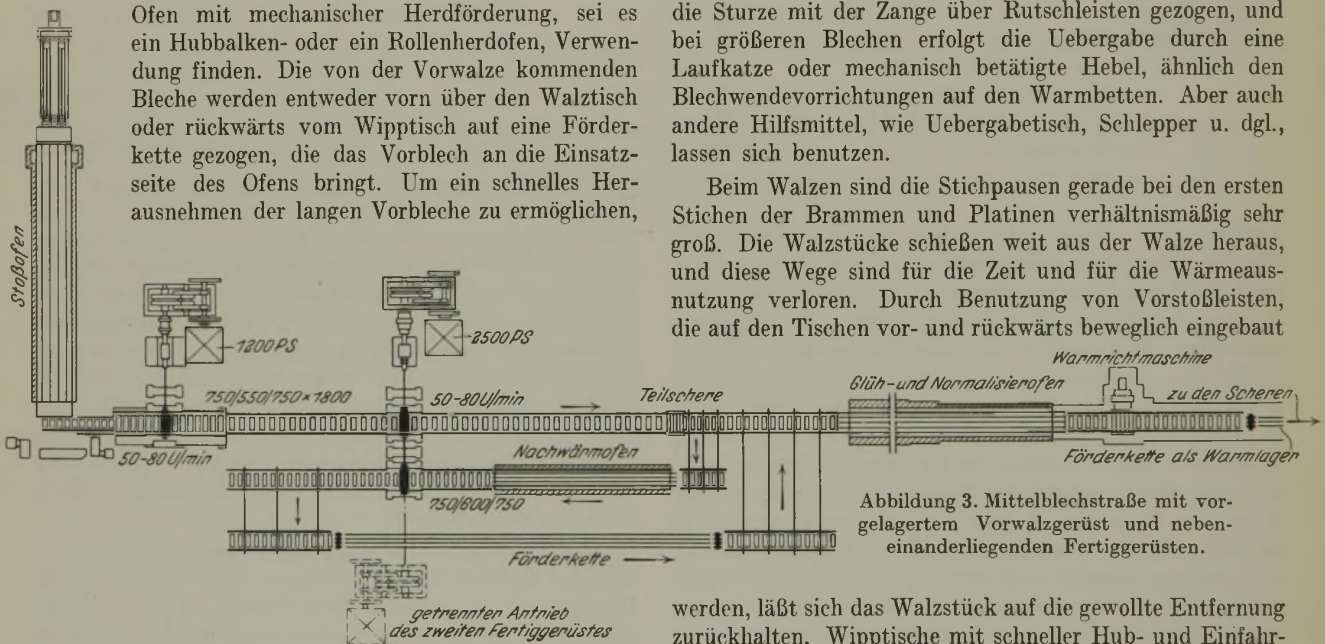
Mittelblechstraße mit vorgelagertem Vorwalzgerüst und nebeneinanderliegenden Fertigerüsten.
